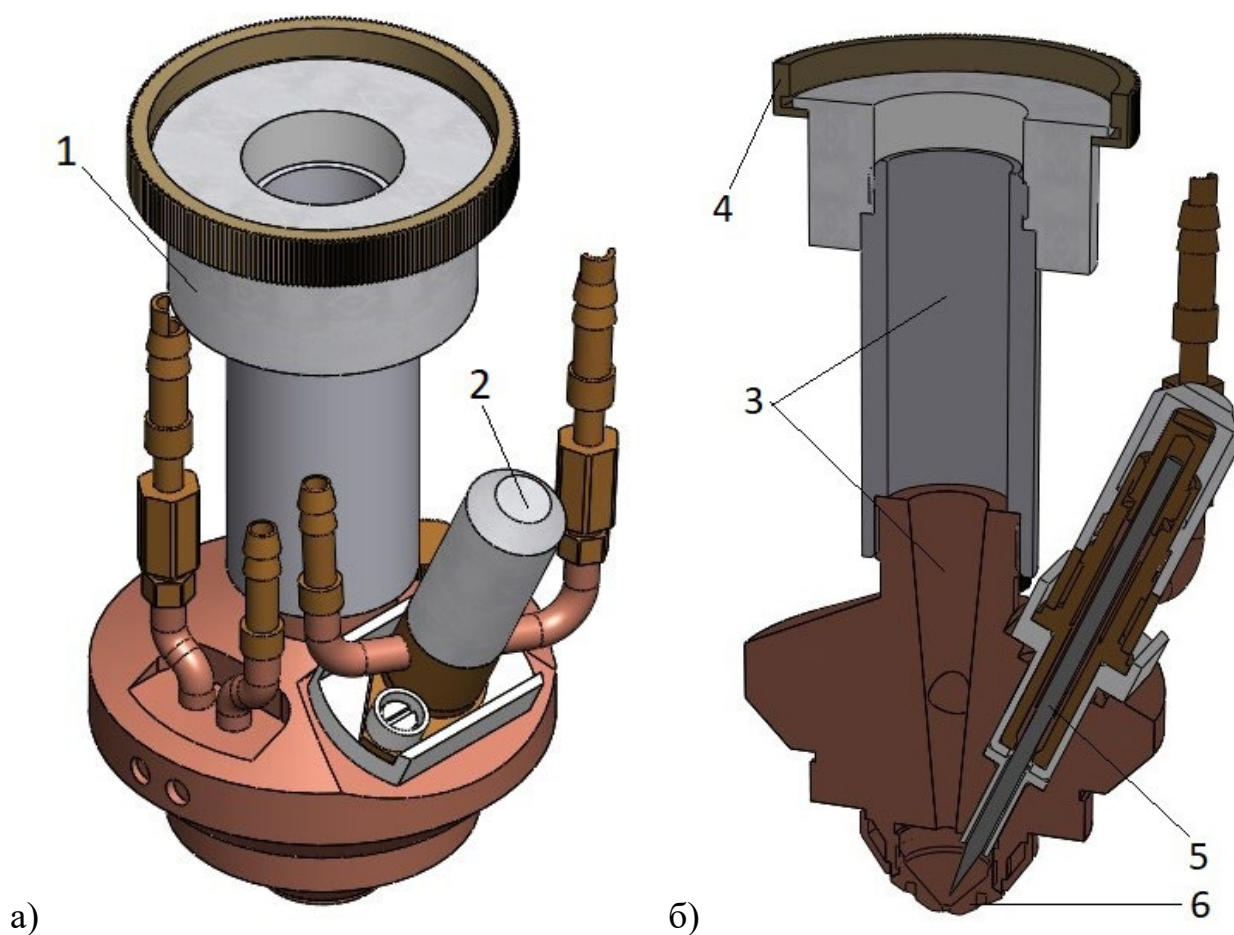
Лазерно-мікроплазмова головка для зварювання в контрольованій атмосфері інертного газу
